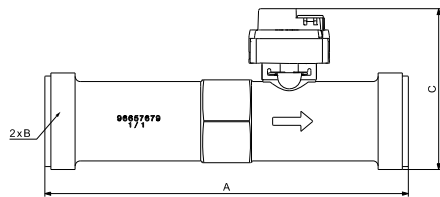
Abmessungen des Sensors MFS 40-400 l/min (ohne Adapter)
